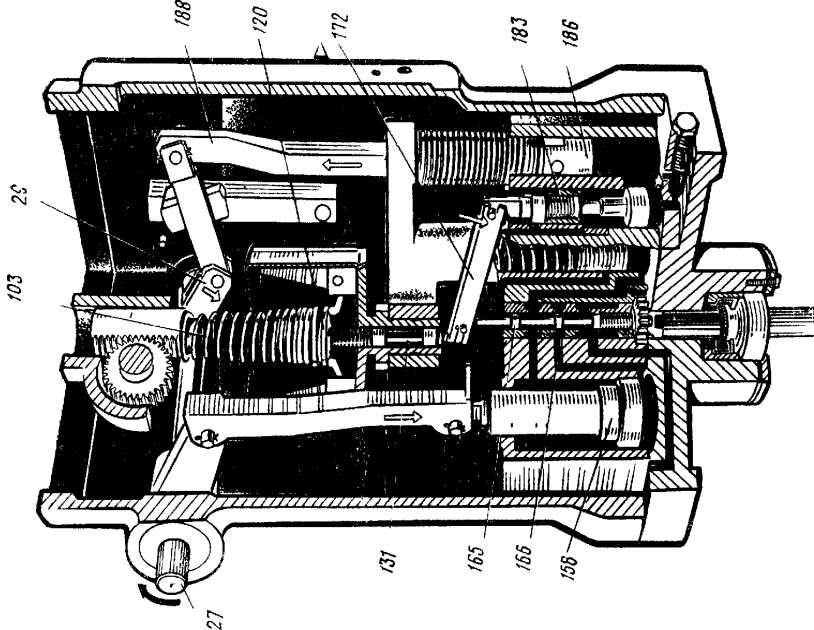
27 — выходной вал; 29 — рычаг изодрома; 103 — задающая пружина; 120 — муфта с подшипником; 131 — шток; 158 — поршень сервомотора; 165 — распределительный золотник; 166 — втулка распределительного золотника; 172 — плавающий рычаг; 183 — пружина изодрома; 186 — принимающий поршень изодрома
